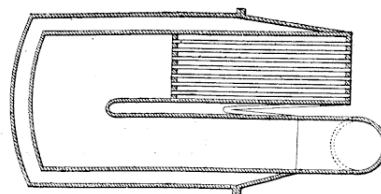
Hackworth. « Sans-Pareille » 1829. Chaudière, plan. »
